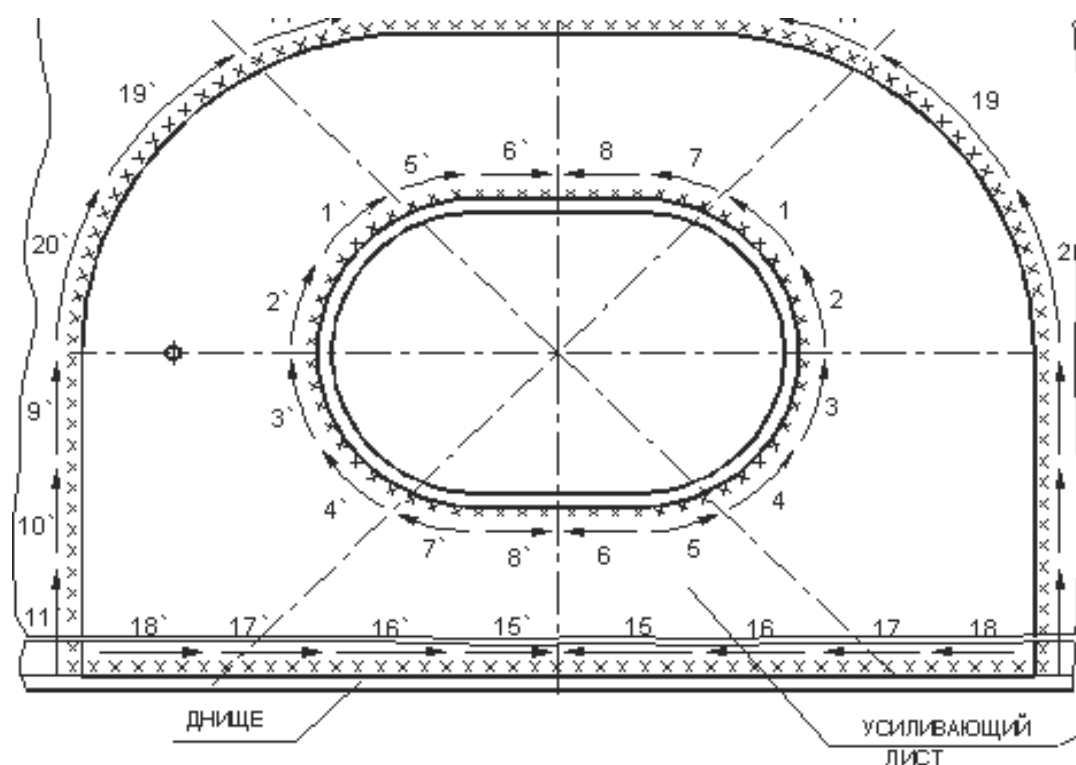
Схема сварки овального люка-лаза с придонным усиливающим листом
